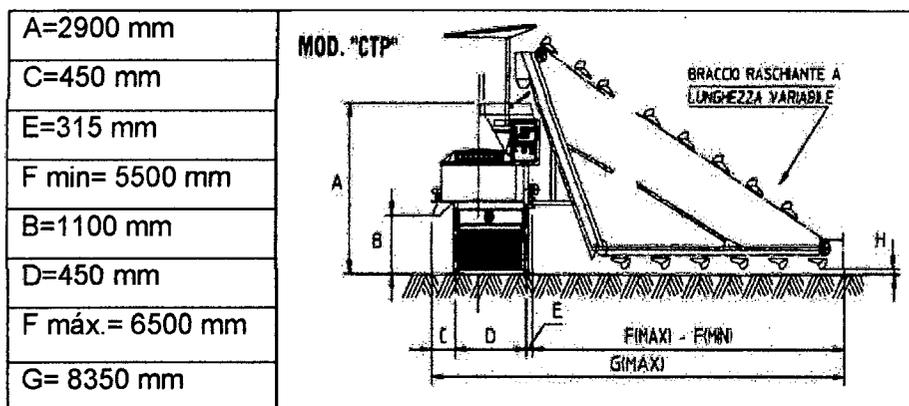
Dimensiones de la planta Piccini MF 400. Fuente Manual de Usuario de la Mini-planta.
